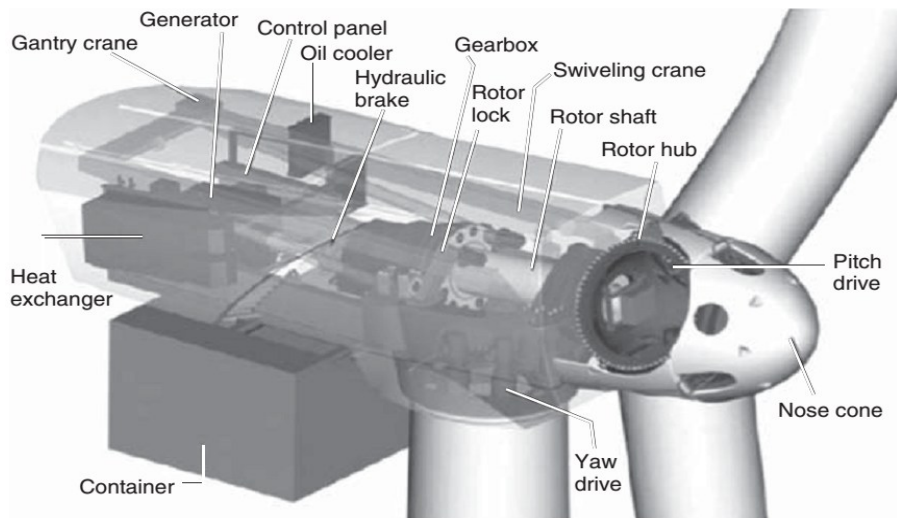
Componentes de una turbina eólica [20]. (Gantry crane: puente grúa. Generator: generador. Control panel: Panel de control. Oil cooler: refrigerador de aceite. Hydraulic brake: freno hidráulico. Gearbox: engranaje. Rotor lock: Bloqueo de rotor. Swiveling crane: puente grúa de rotor. Rotor shaft: eje del rotor. Rotor hub: rotor central. Pitch drive: transmisión. Nose cone: nariz en forma de cono. Yaw drive: corona de orientación. Container: contenedor. Heat exchanger: intercambiador de calor.)
